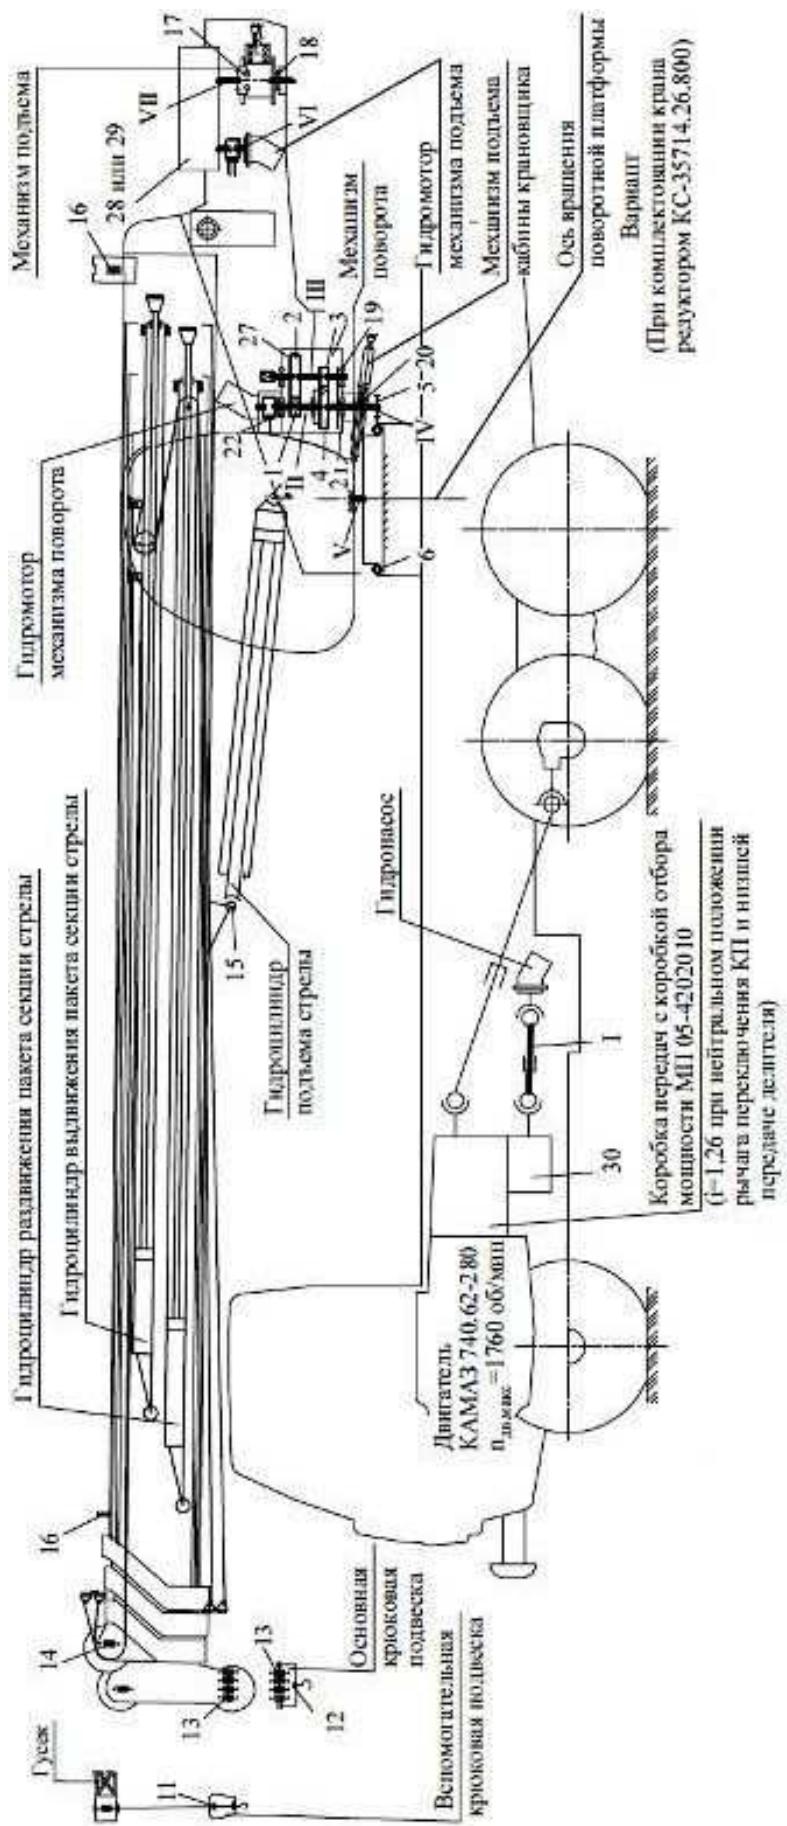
Схема кинематическая принципиальная: I-VII – валы, 1-10 – валы-шестерни, зубчатые колеса, 11-26 – подшипники, 27-30 – редукторы
